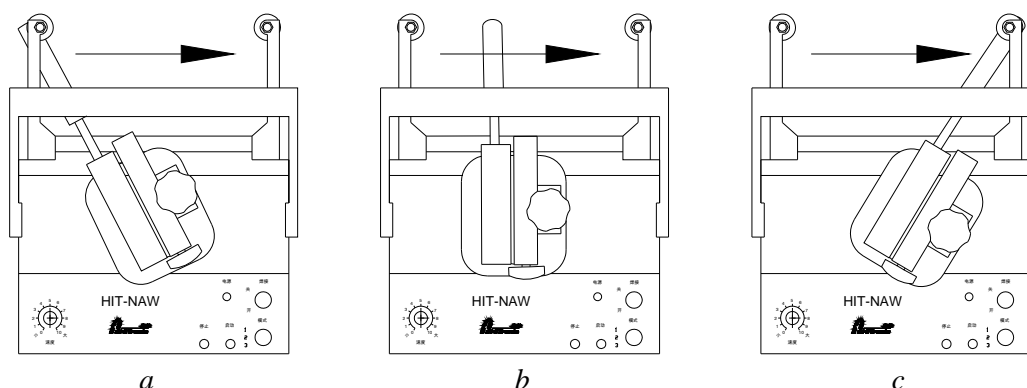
Последовательность работы сварочной каретки HIT-NAW
